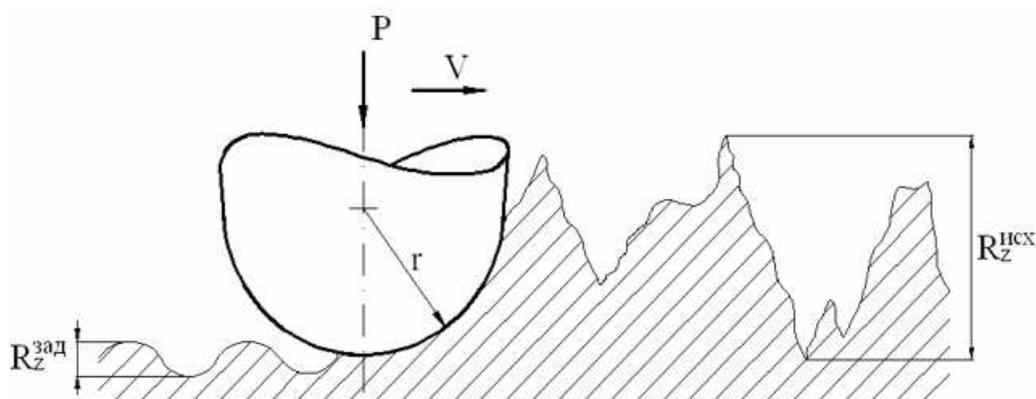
Формирование низкой шероховатости обрабатываемой поверхности
